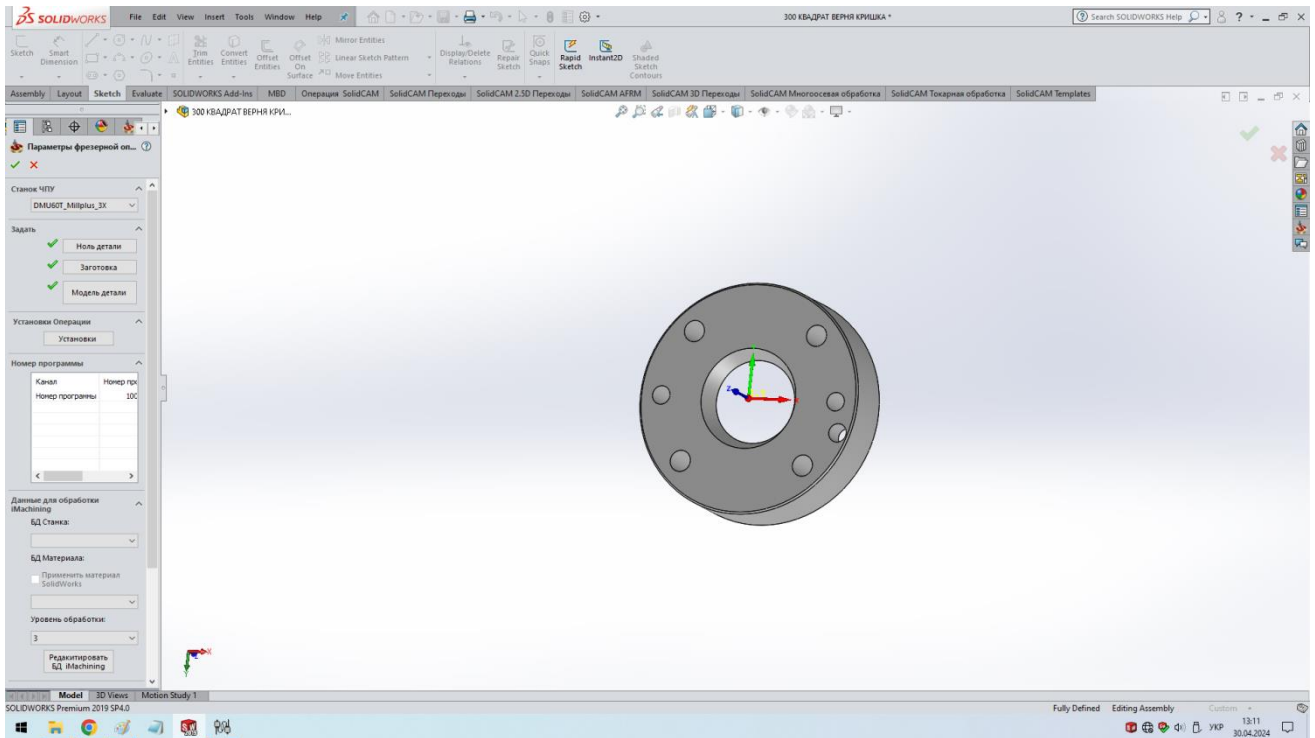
3D модель кришки та параметри для фрезерної обробки
